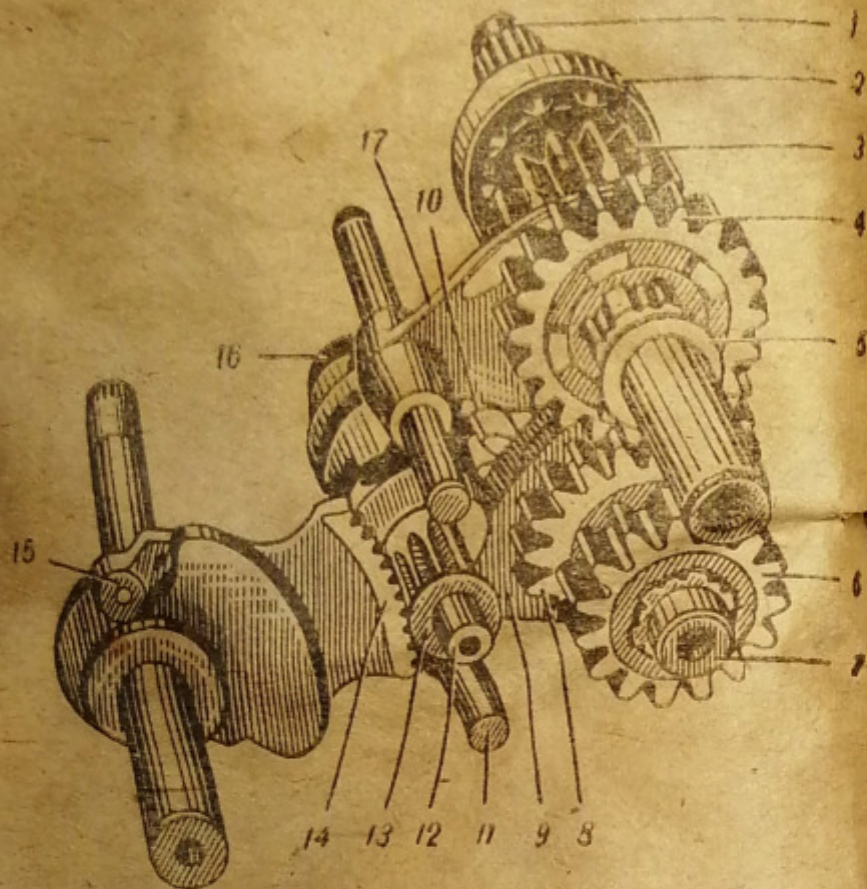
КОРОБКА ПЕРЕДАЧ:
